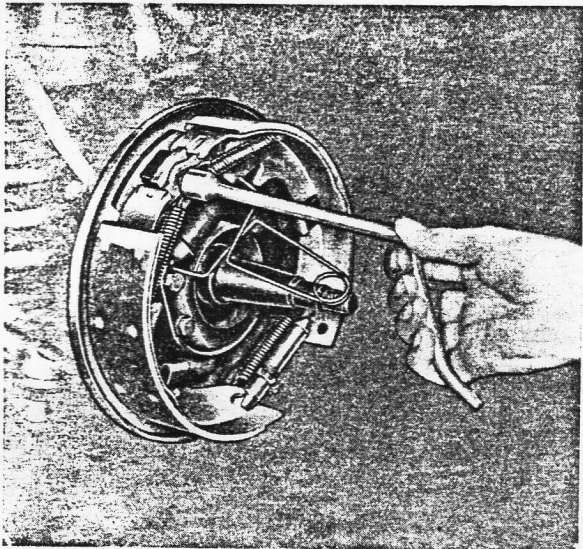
Ausbau der Rückholfeder mit einem Bremsfederwerkzeug (Snap-on BT 11 oder entsprechendes)
